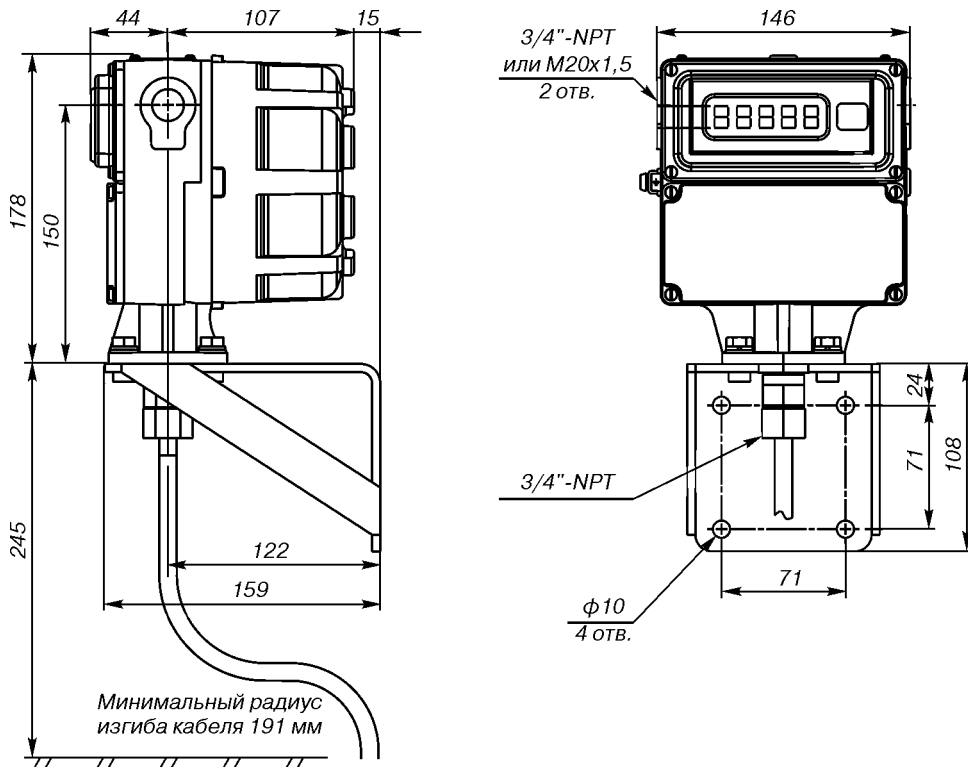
Габаритные и присоединительные размеры преобразователей IFT9701, IFT9703 при удаленном монтаже.
